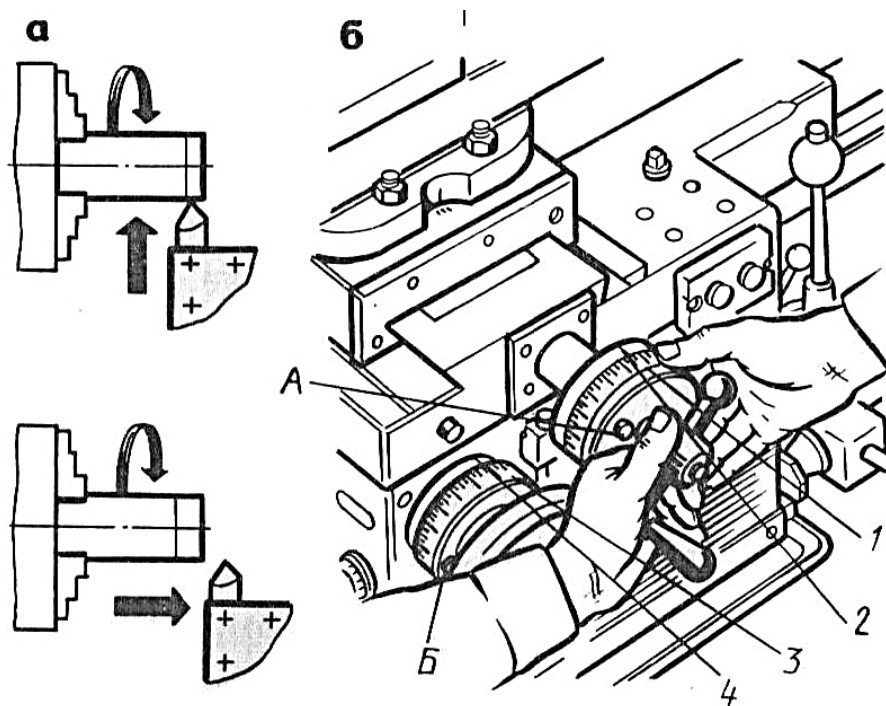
Приём установки резца на глубину резания: 1 – кольцо лимба поперечной подачи; 2 – риска на неподвижной втулке винта поперечной подачи; 3 – кольцо лимба продольной подачи; 4 – риска на неподвижной втулке винта продольной подачи; А, Б – стопорные винты лимбов
